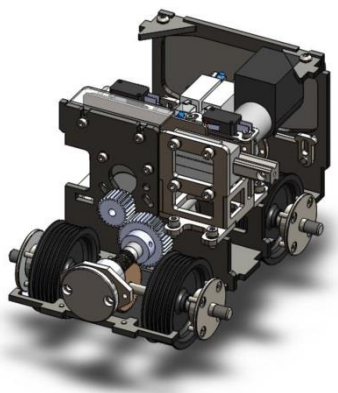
Configuração utilizando a transmissão de movimento por engrenagem.
